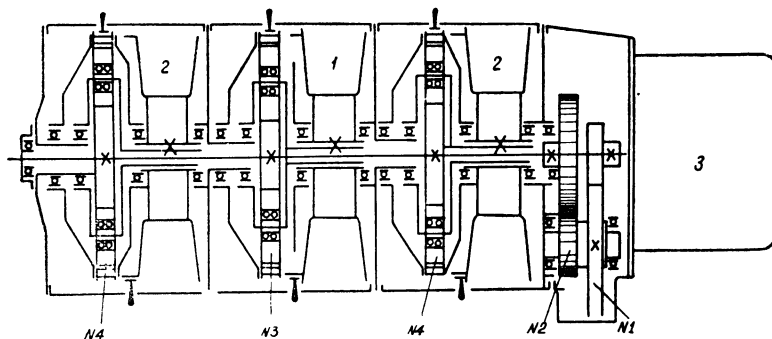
Кинематическая схема скреперной лебедки 3ЛСЭ-28:
